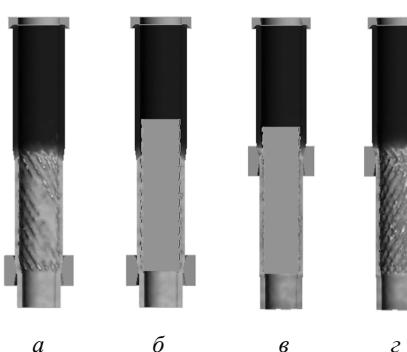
Моделирование технологического процесса редуцирования трубной заготовки в программной среде QForm 7: *а* – получение буртика; *б* – установка оправки с много-заходными спиральными выступами встречного направления; *в* – редуцирование трубной заготовки с оправкой; *г* – трубная заготовка с внутренними спиральными рифлениями после 1-го перехода 2-го редуцирования
